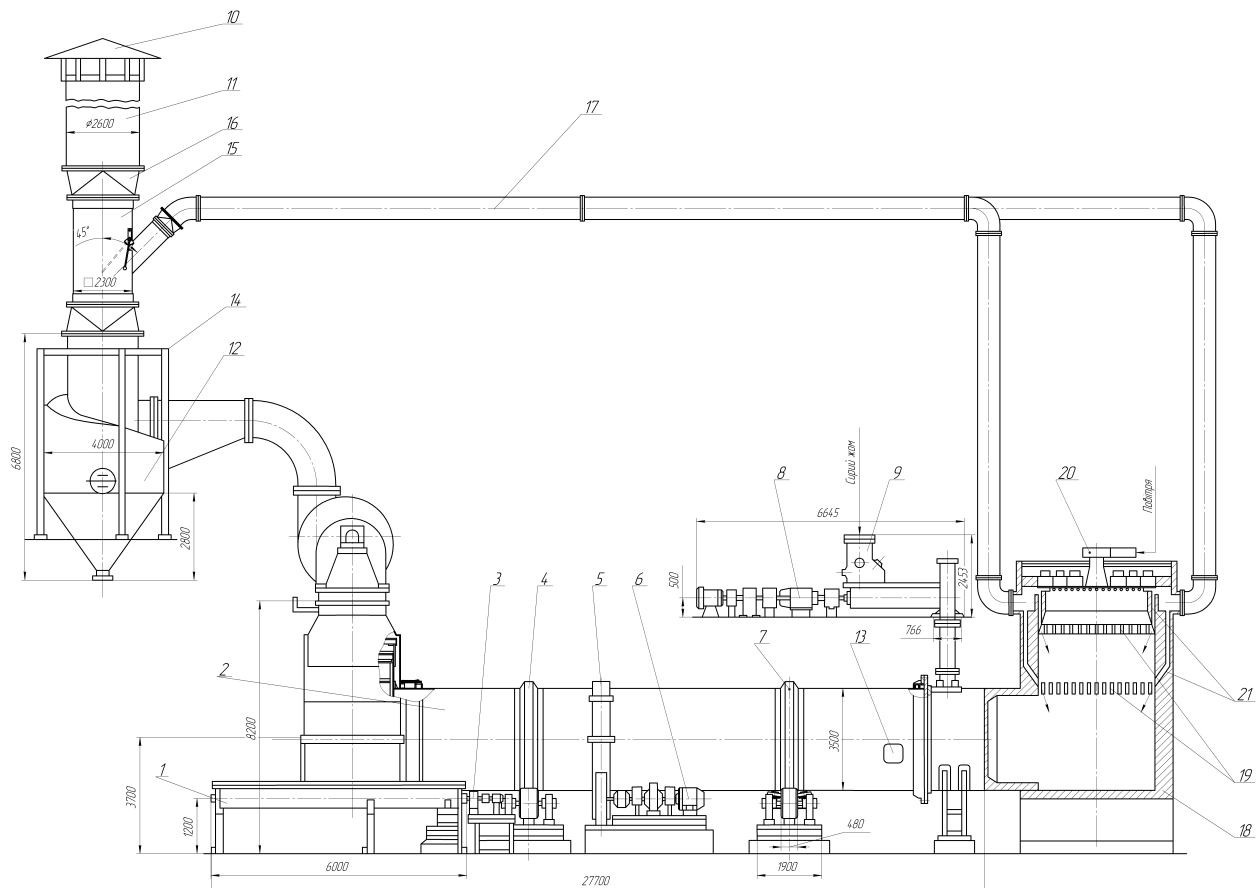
Барабан жомосушильний марки А2-ПСА
